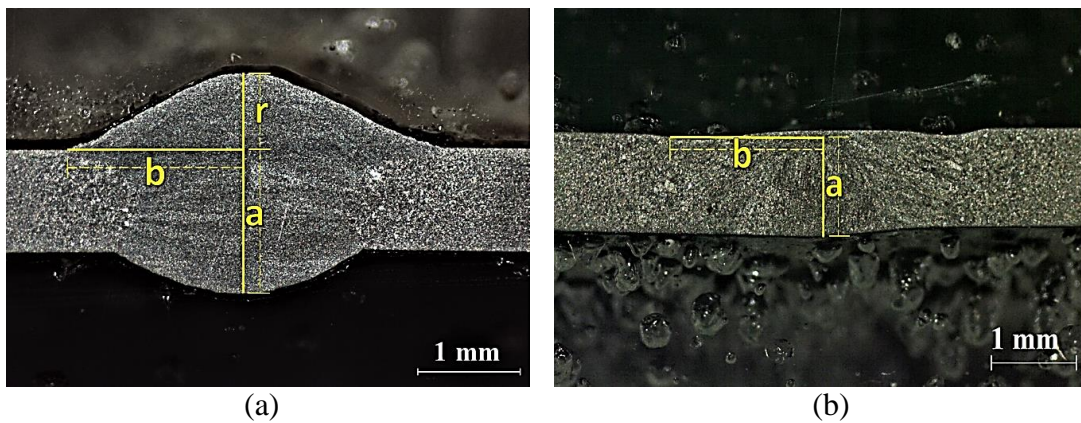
6 – Esquema das dimensões da seção transversal de cordão de solda. a) soldas MAG. b) soldas TIG.
